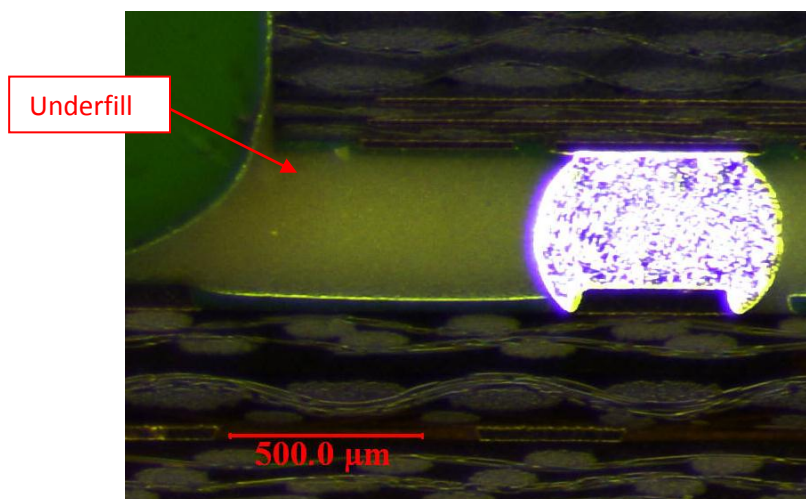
Vue en coupe de l'underfill au second niveau d'interconnexion
